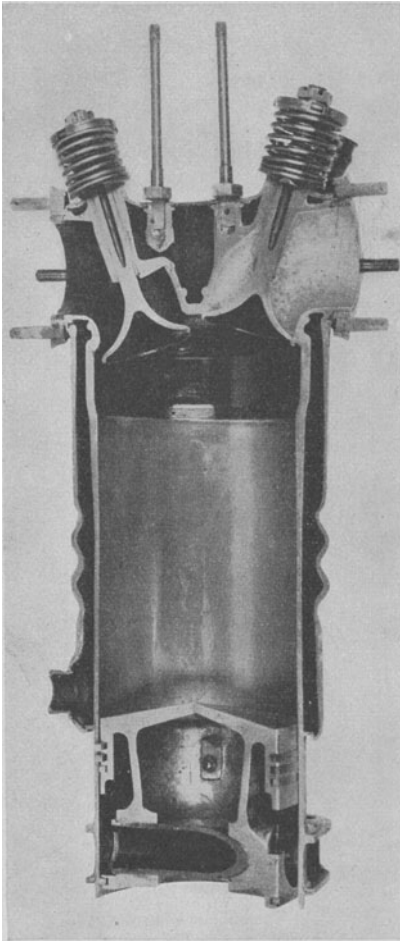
Zylinder des Rolls-Royce-Flugmotors.
